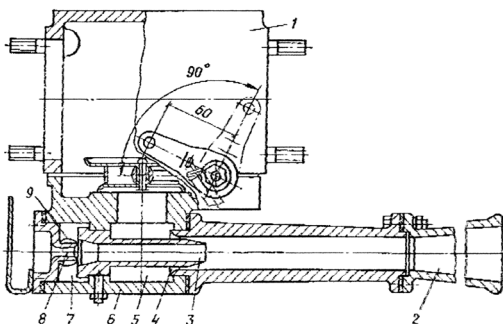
Двухступенчатый газоструйный вакуумный аппарат:
